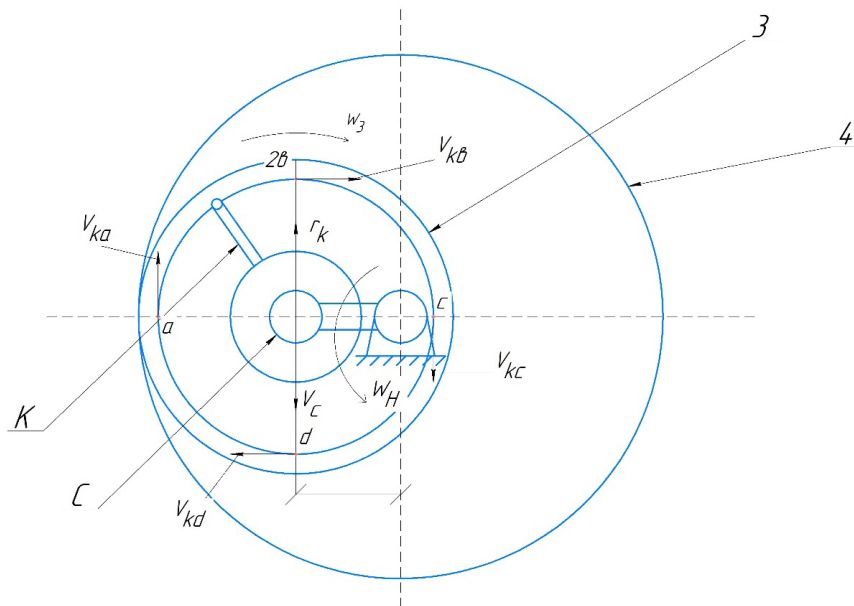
Вид сверху на планетарный привод Шумахера
